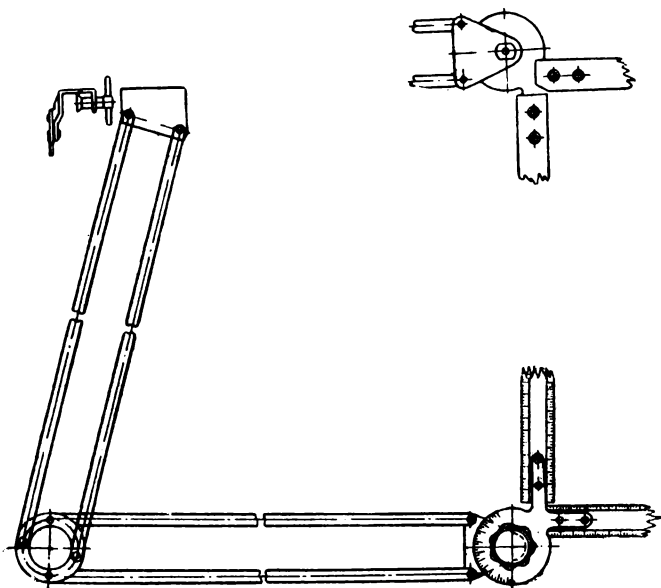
Настольный чертежный прибор ЧПГ.
